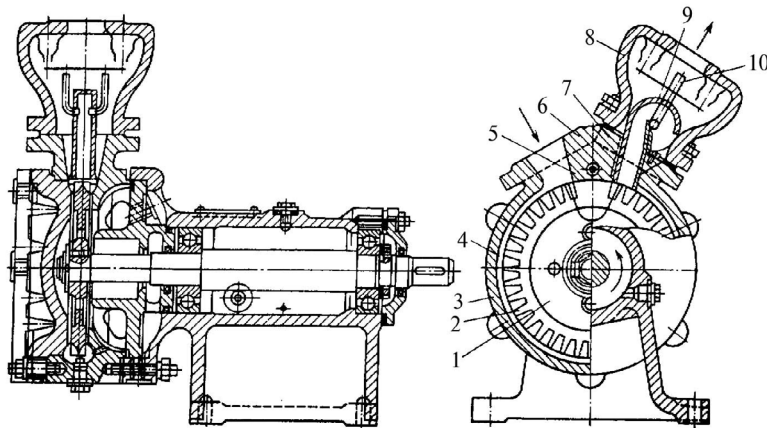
Конструкція вихрового насоса: 1 – робоче колесо; 2 – лопаті робочого колеса; 3 – корпус; 4 – концентричний кільцевий канал; 5 – роздільна перемичка; 6 – усмоктувальний патрубок; 7 – нагнітальний патрубок; 8 – вузол самоусмоктування; 9 – ковпак; 10 – повітряпровід.
